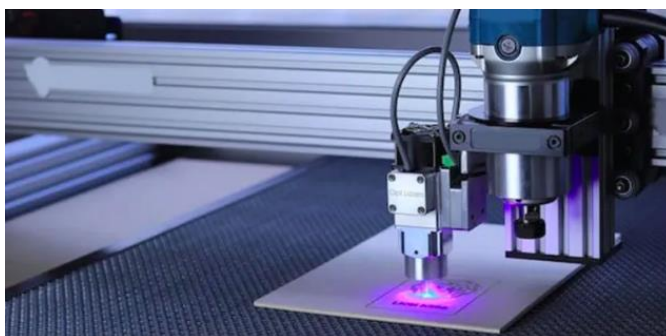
Máquina de corte por láser. Extraído de <https://www.lasertechnologies.co.in>.
